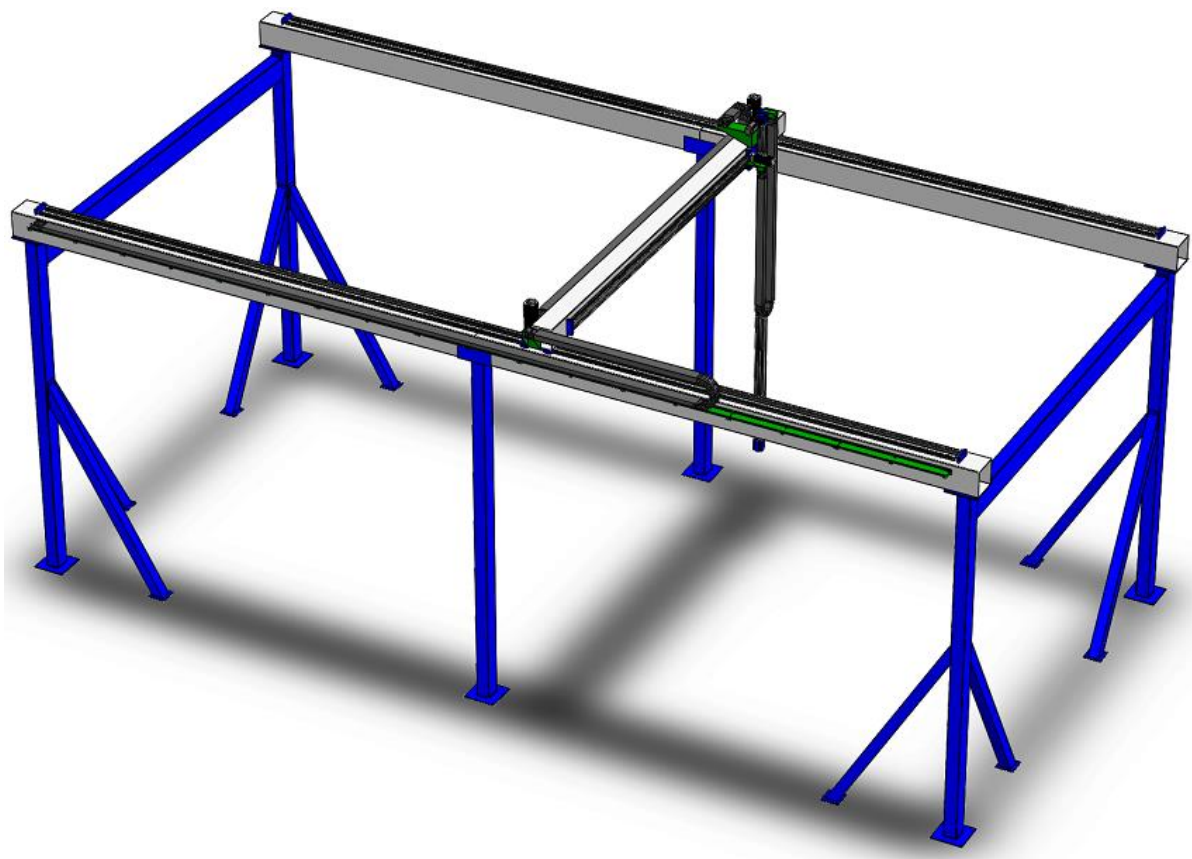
CAD del diseño detallado de la impresora 3D.
